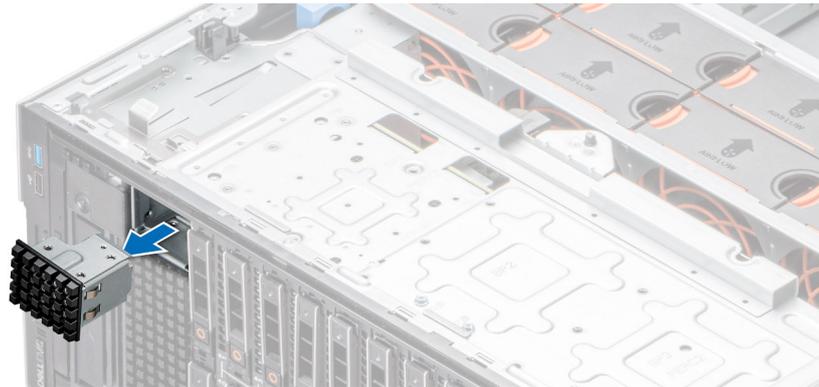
Entfernen des Platzhalters aus dem BOSS-S2-Modul
